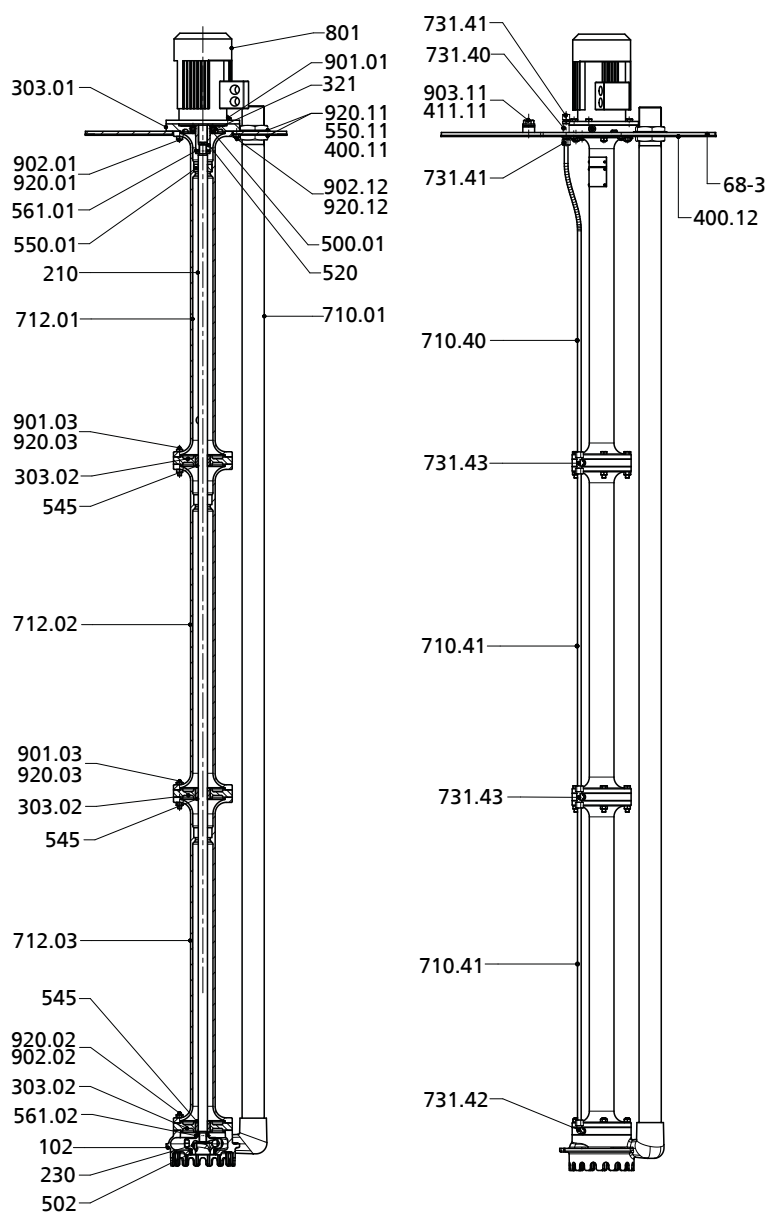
Plano de sección MK, MKA - Profundidad de montaje 2.800 mm - Lubricación con otro líquido
